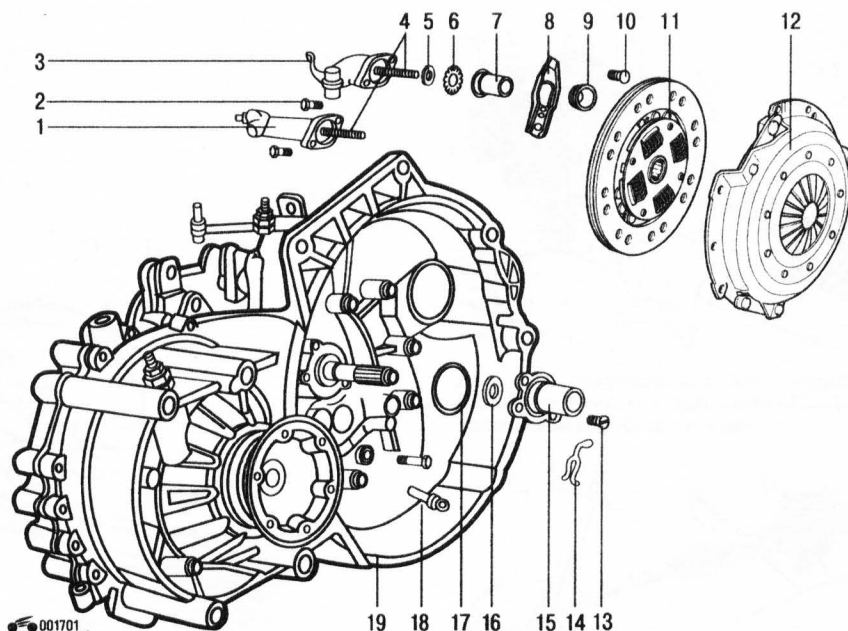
Сцепление: 1 – рабочий цилиндр гидравлического привода выключения сцепления; 2 – крепежный болт; 3 – рычаг механического (тросового) привода выключения сцепления; 4 – толкатель; 5 – уплотнительная шайба (механический привод выключения сцепления); 6 – зубчатая шайба (механический привод выключения сцепления); 7 – направляющая втулка подшипника выключения сцепления; 8 – рычаг выключения сцепления; 9 – подшипник выключения сцепления; 10 – болт; 11 – ведомый диск; 12 – кожух сцепления; 13 – болт крепления направляющей втулки подшипника выключения сцепления; 14 – пружинный фиксатор; 15 – направляющая втулка; 16 – уплотнительное кольцо первичного вала; 17 – уплотнительная шайба; 18 – шпилька с шаровым наконечником; 19 – картер коробки передач
